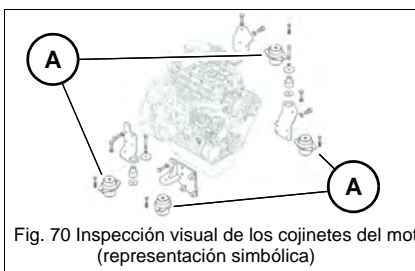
Inspección visual de los cojinetes del motor (representación simbólica)
